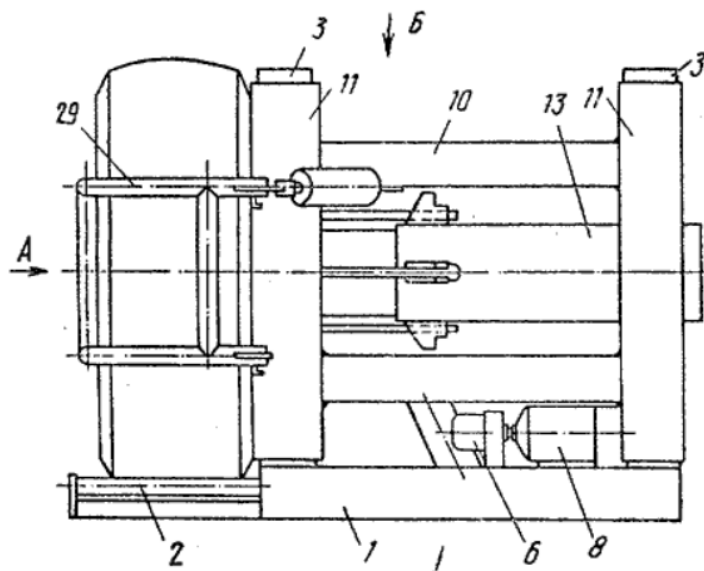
Шиномонтажный стенд, вид сбоку
